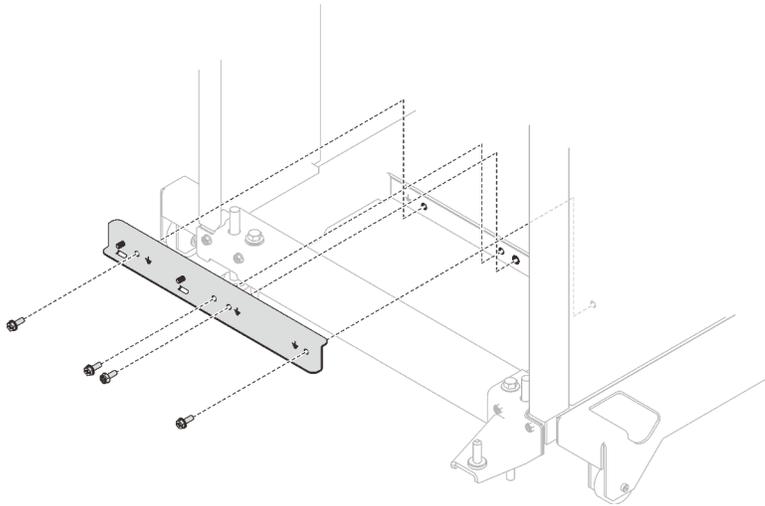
Installation der unteren Montagehalterung für die Rackleitung
